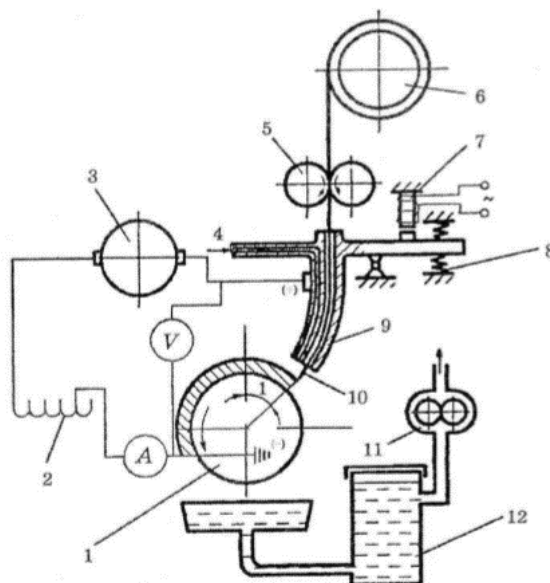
Схема установки для вібродугового наплавлення деталей
